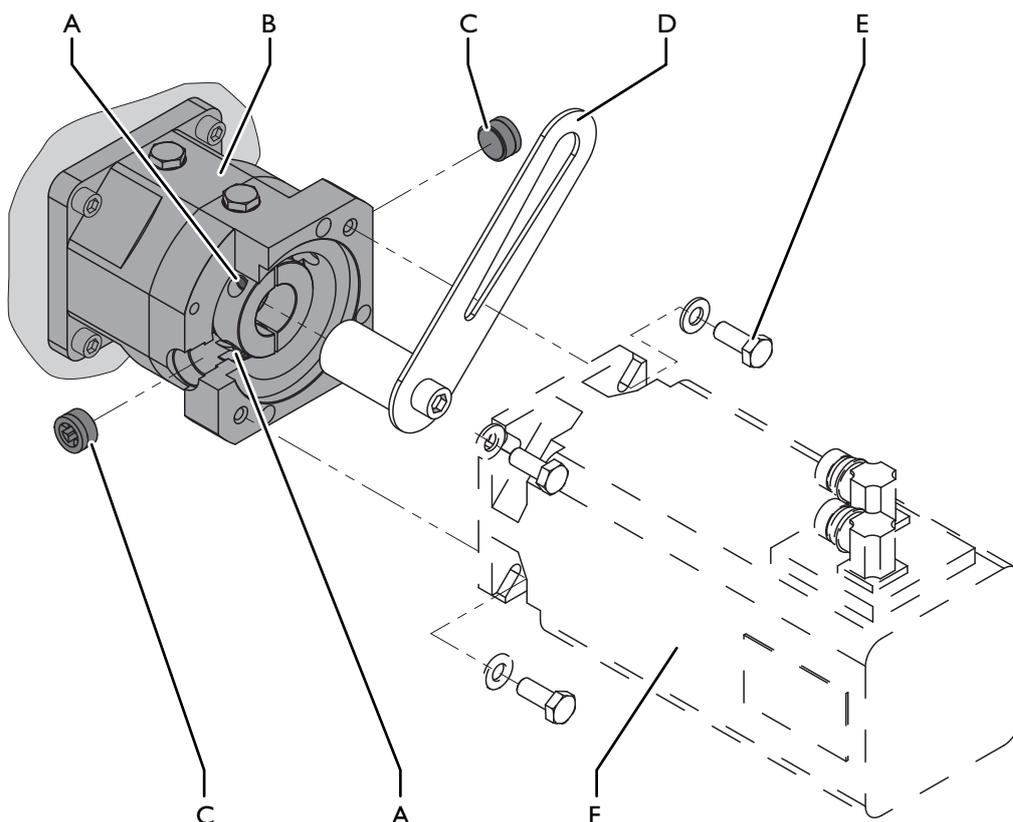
Установить транспортное крепление: Планетарный редуктор Güdel
